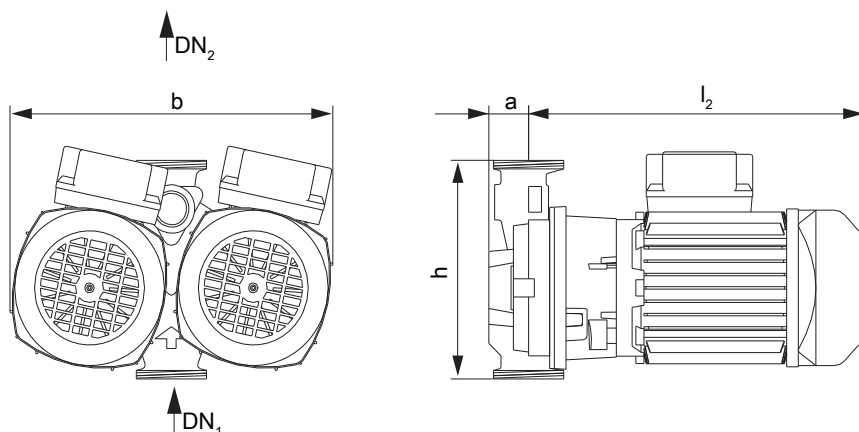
Размеры насосного агрегата с резьбовым соединением, типоразмер 032-032-080
